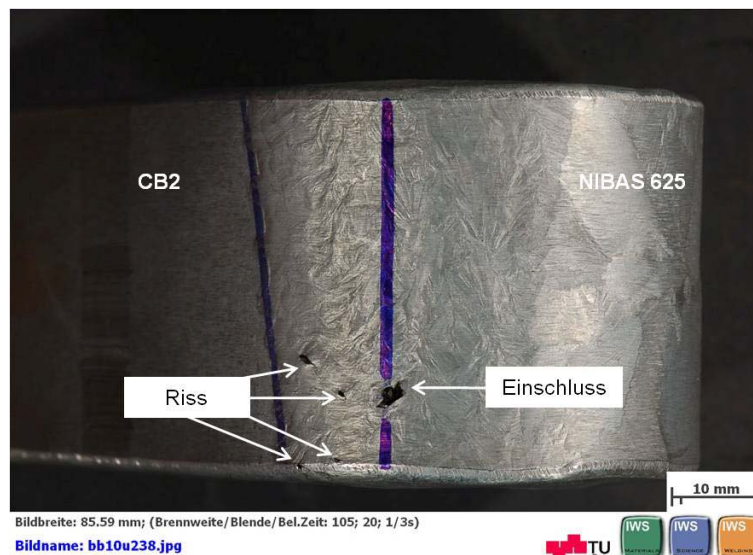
Gebogene Seitenbiegeprobe (3. Probeschweißung - Massivdrahtelektrode); geführter Seitenbiegeversuch.
